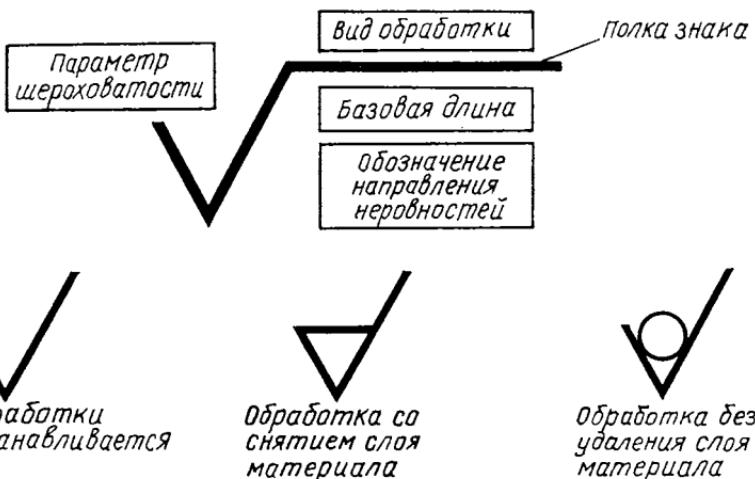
Знаки, обозначающие шероховатость поверхности на чертежах.
